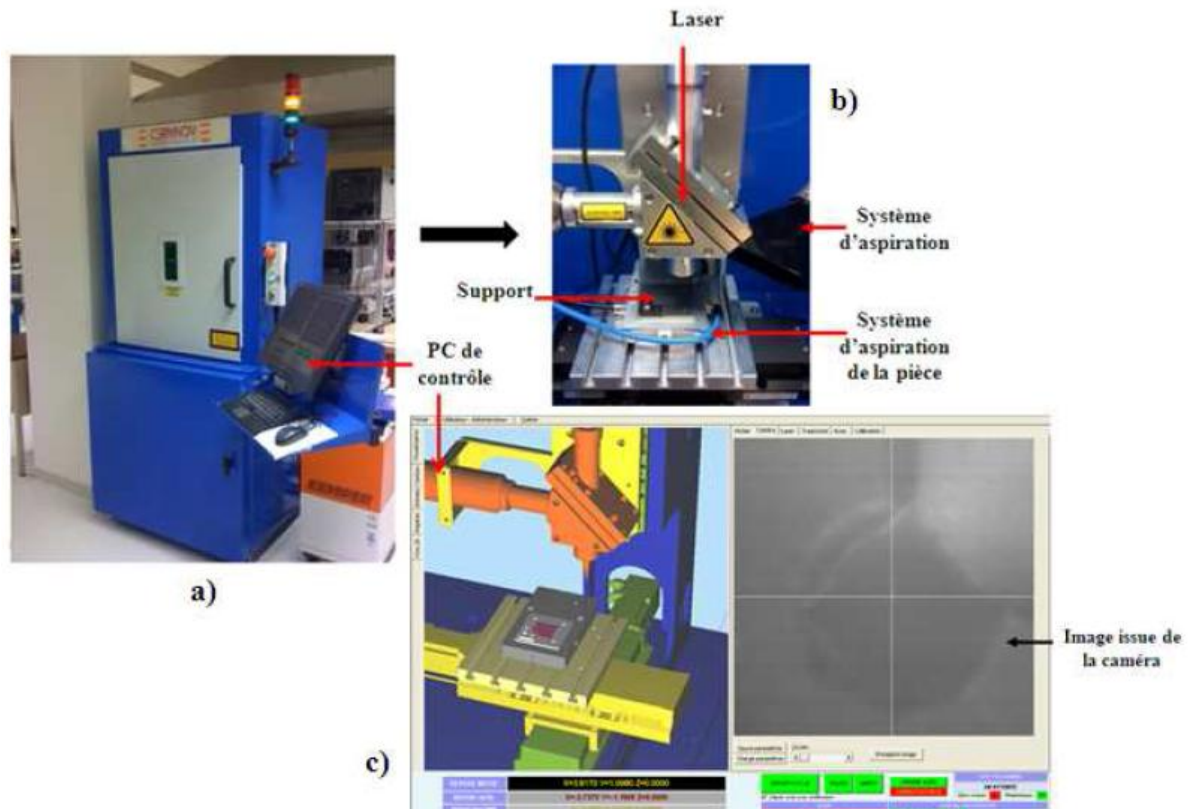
Machine laser Cerinnov a) vue extérieure ; b) vue intérieure ; c) interface du logiciel de contrôle de la machine.
